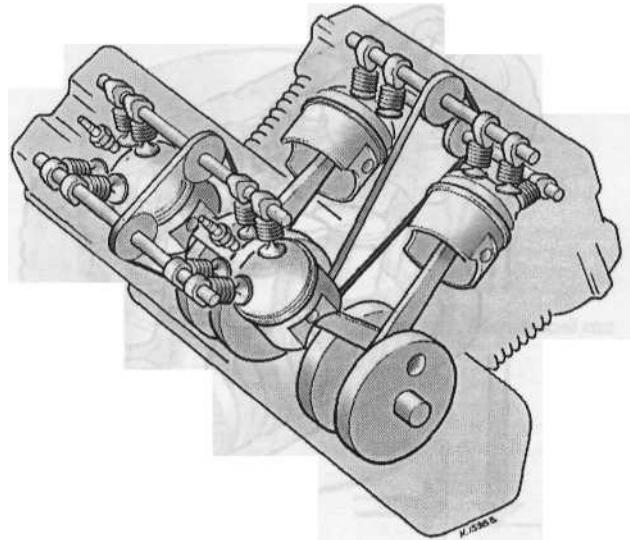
д Четырехтактный V-образный четырехцилиндровый двигатель
